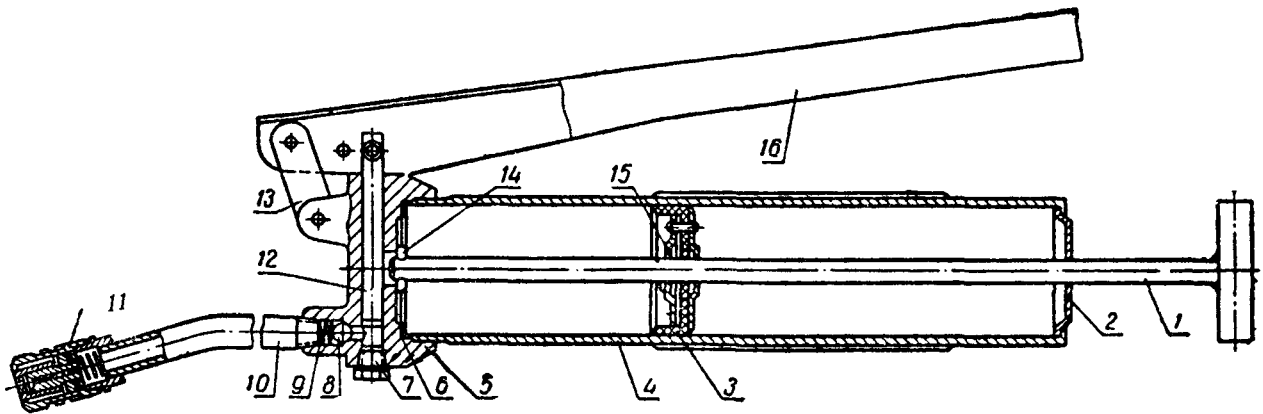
Рычажно-плунжерный шприц для консистентной смазки:
